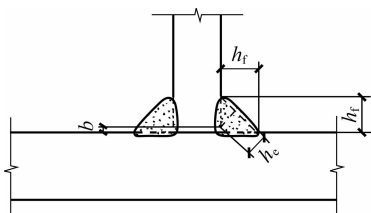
直角角焊缝及搭接角焊缝计算厚度
